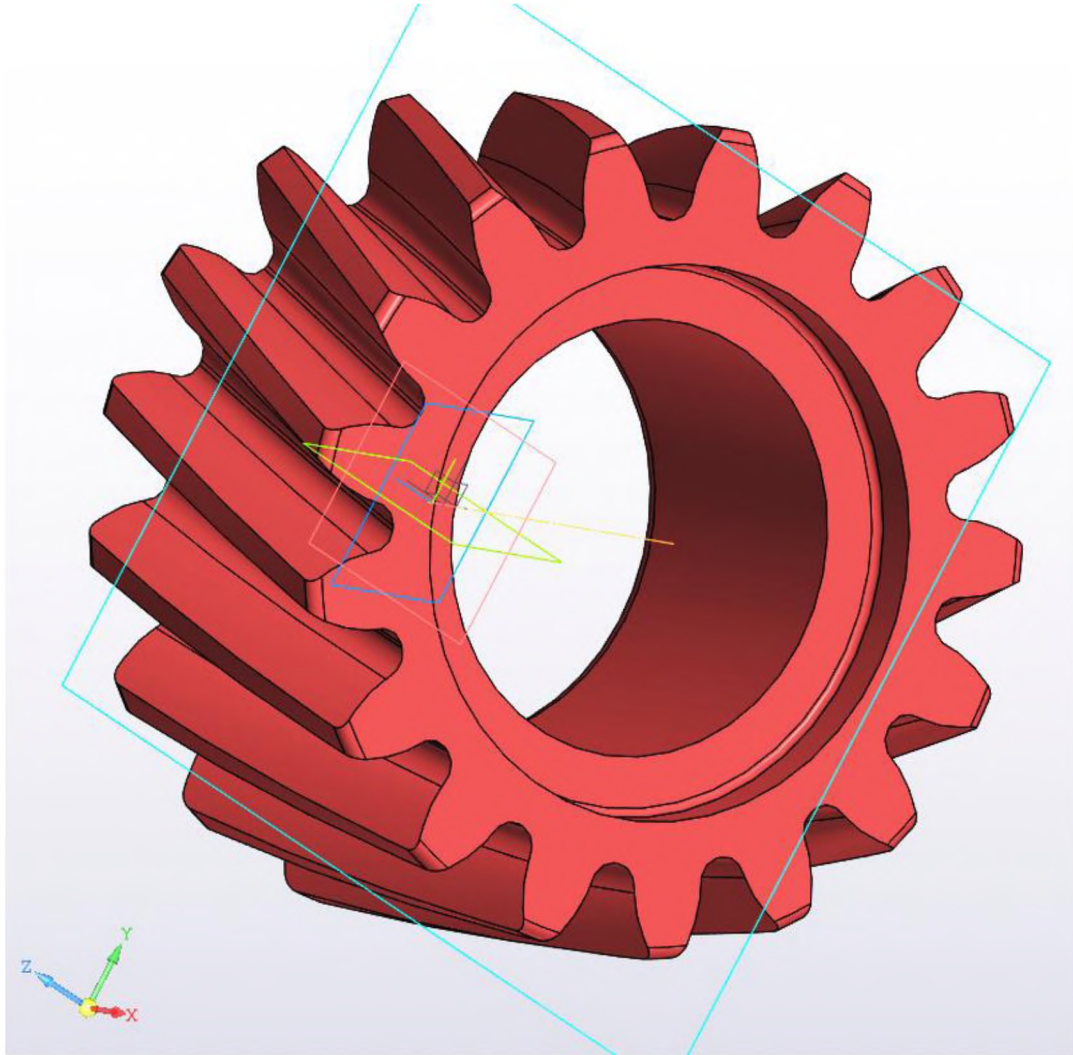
Креслення 3D деталі «Шестерня»
